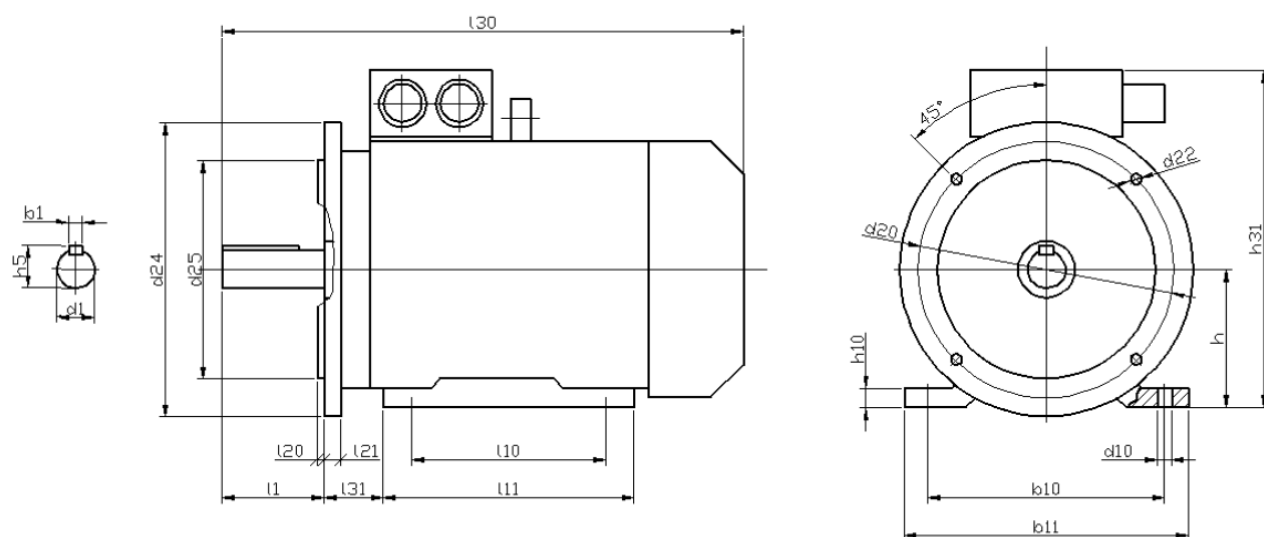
Габаритные и присоединительные размеры двигателя
